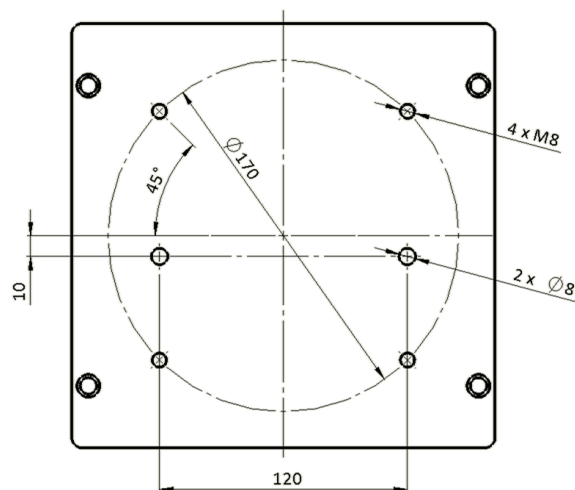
Spoj robot Universal robots UR 16E - zdviž
